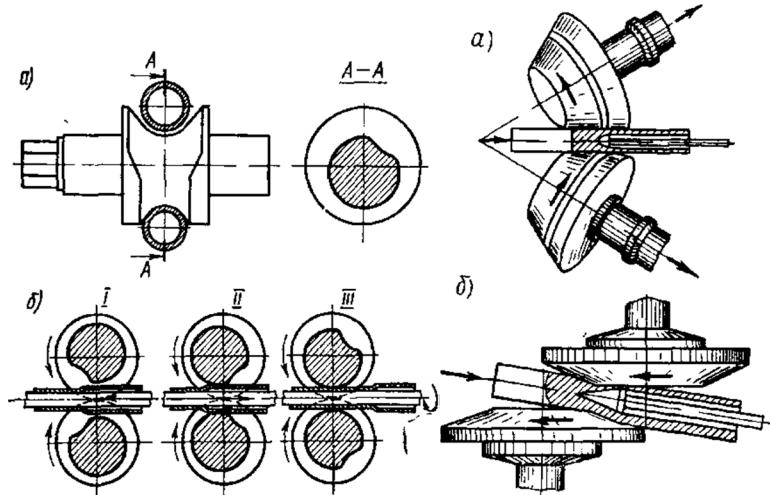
Схема пилигримовой прокатки за один оборот валков:
